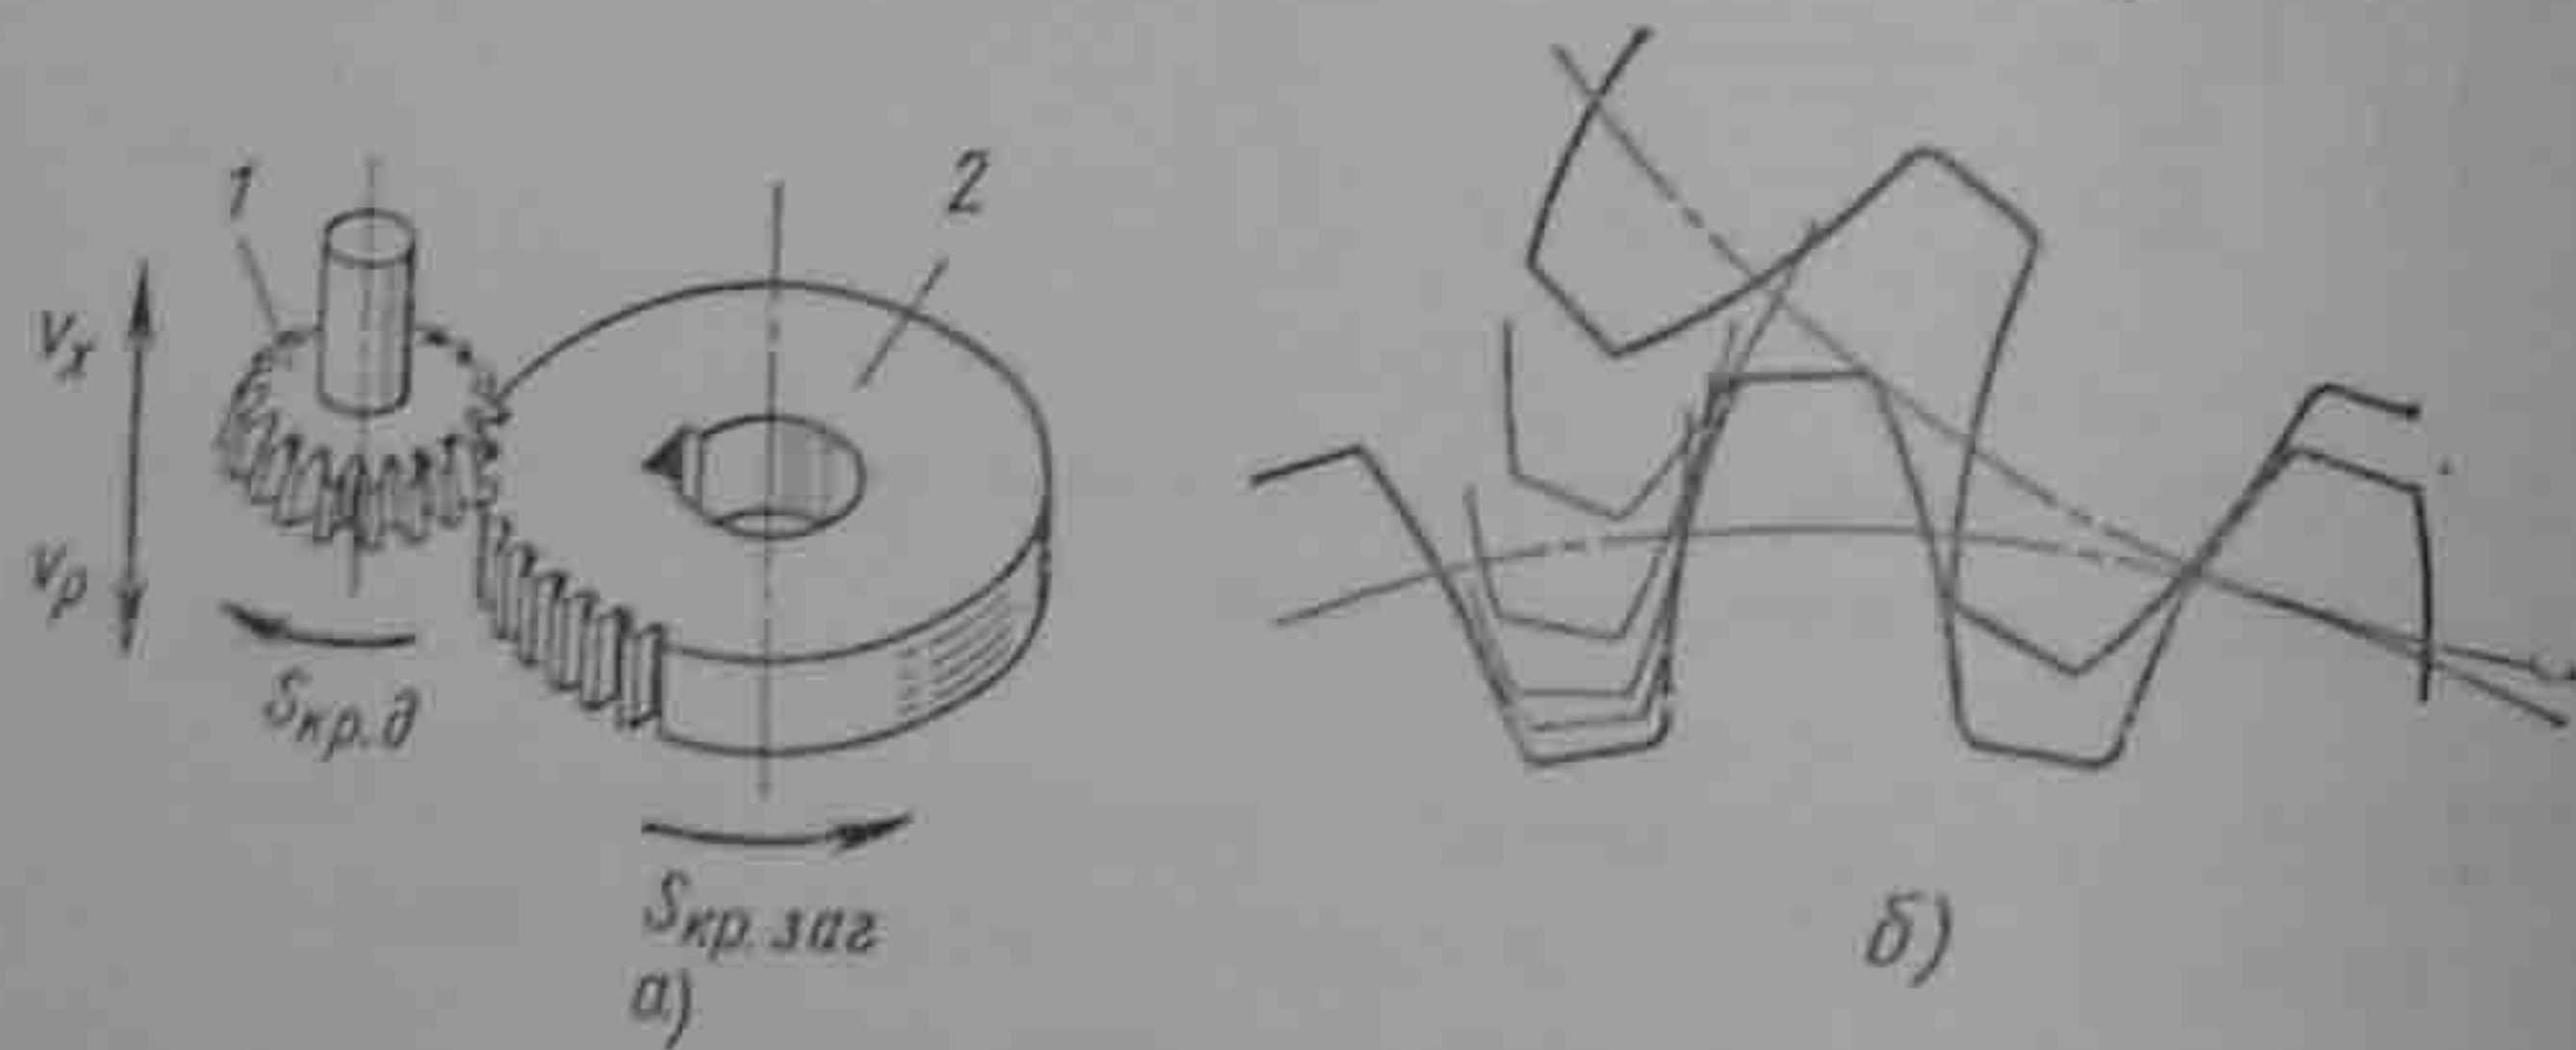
Схема формообразования зубьев цилиндрического колеса долбяком:
